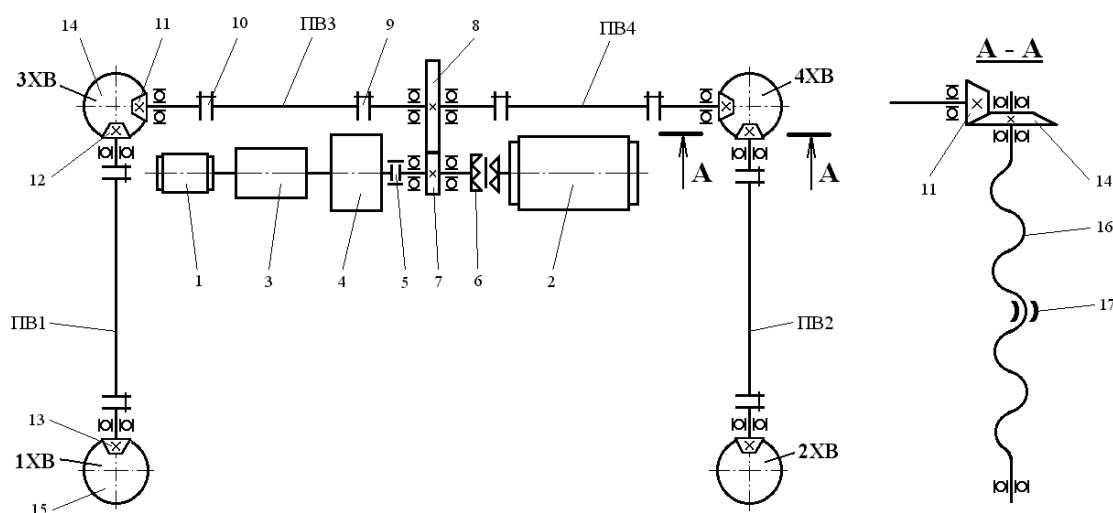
Кинематическая схема привода вертикальной подачи пильной рамы штрипсового станка: 1 – электродвигатель рабочей подачи; 2 – электродвигатель ускоренной подачи; 3 – система вариаторного регулирования; 4 – планетарный редуктор; 5 – зубчатая муфта; 6 – кулачковая муфта; 7,8 – цилиндрические зубчатые колёса (цилиндрический редуктор); 9 – втулочная муфта; 10 – дисковая муфта; 11, 12,13 – коническая вал-шестерня; 14,15 – коническое зубчатое колесо; 16 – ходовой винт; 17 – ходовая гайка
